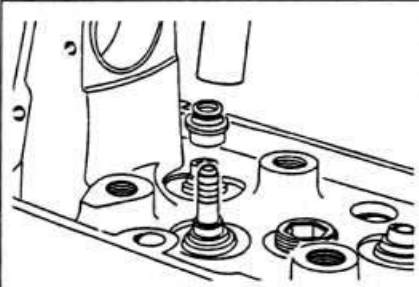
Установка маслоотражательного колпачка на стержень клапана
